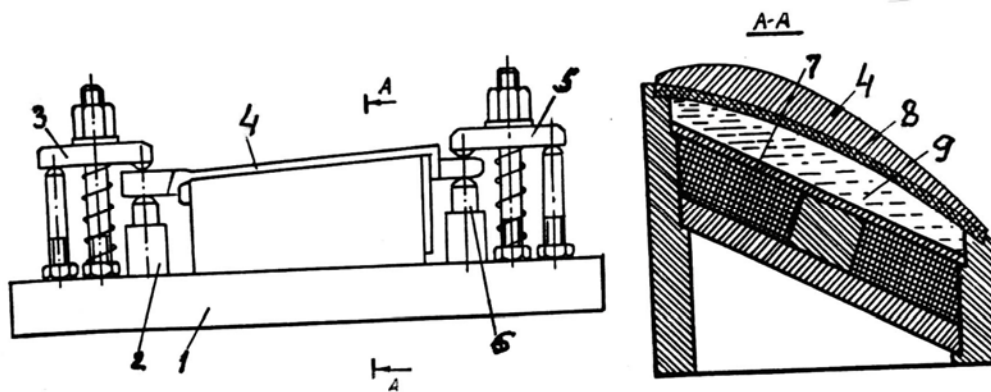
Схема закріплення заготовок з невеликою жорсткістю при виконанні свердильних і фрезерних робіт
